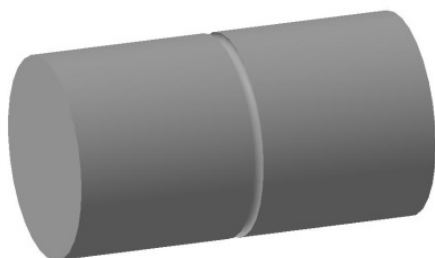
Цилиндрическая деталь с круговым надрезом полукруглого профиля
